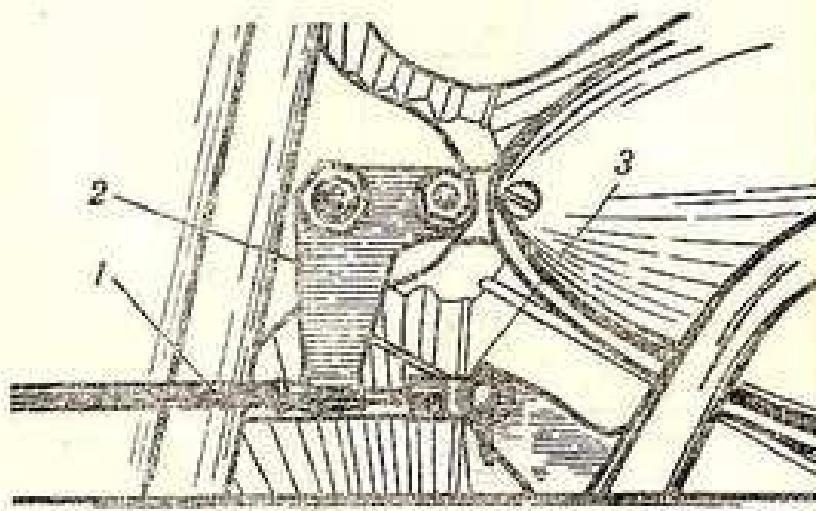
УСТАНОВКА ТРОСА ТОРМОЗА:
